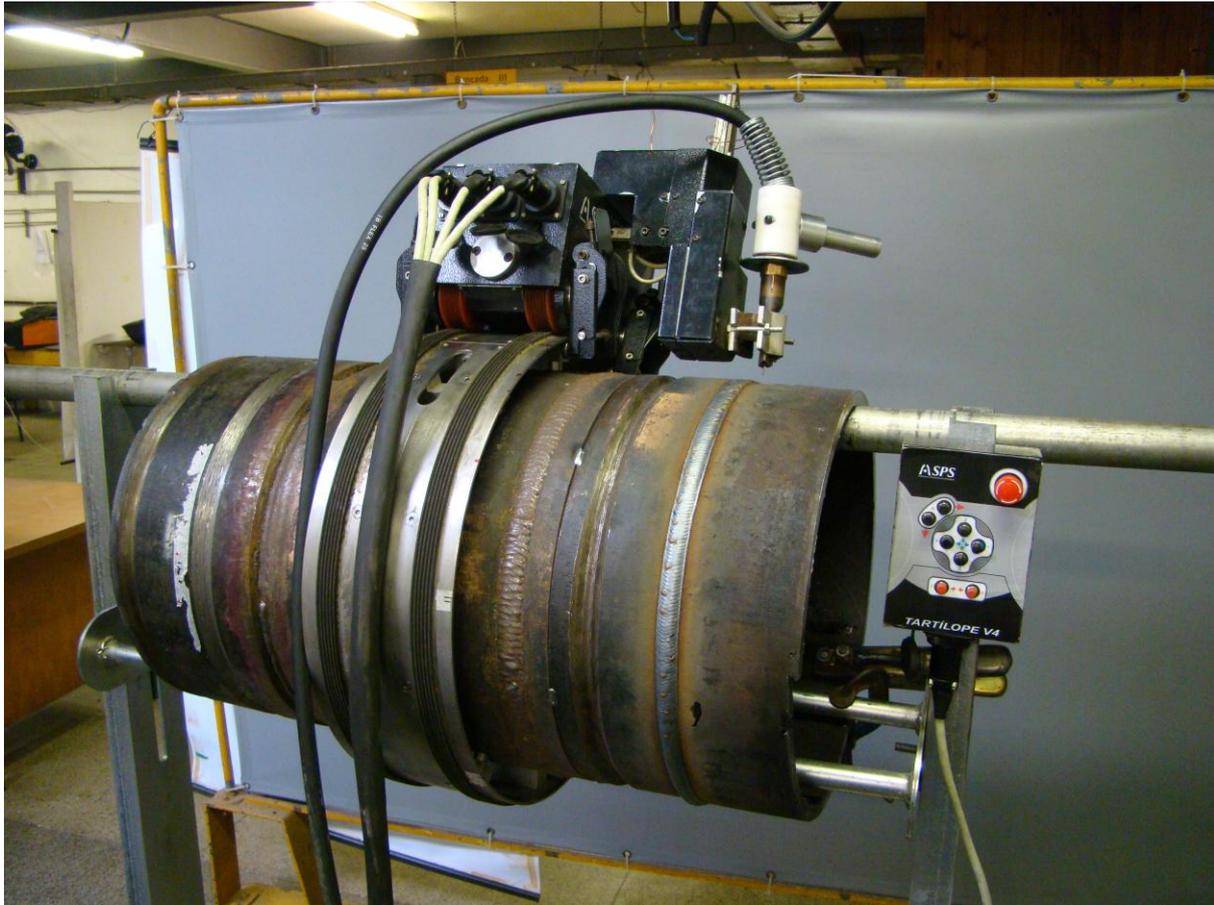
Suporte de dutos para a realização dos testes de soldagem orbital.
